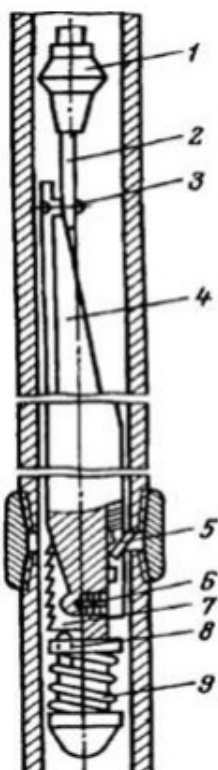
Схема отклонителя висячего типа, устанавливаемого на стыке труб: 1 – райбер; 2 – направление; 3 – болт; 4 – отклонитель; 5 – защелка; 6 – фиксатор; 7 – плашка; 8 – шток; 9 – пружина
